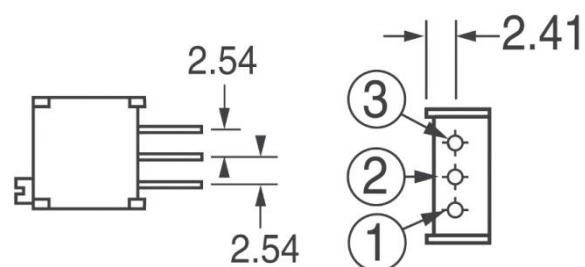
Габаритні розміри резистора 3296P-1-102LF
